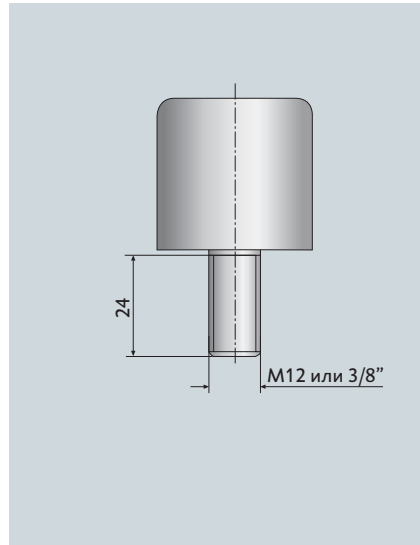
Разъединитель линии заземления Код заказа Р31, вес 0,1 кг
